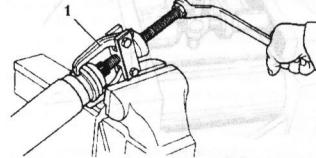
Снимите подшипник с вала при помощи вытаскивателя
